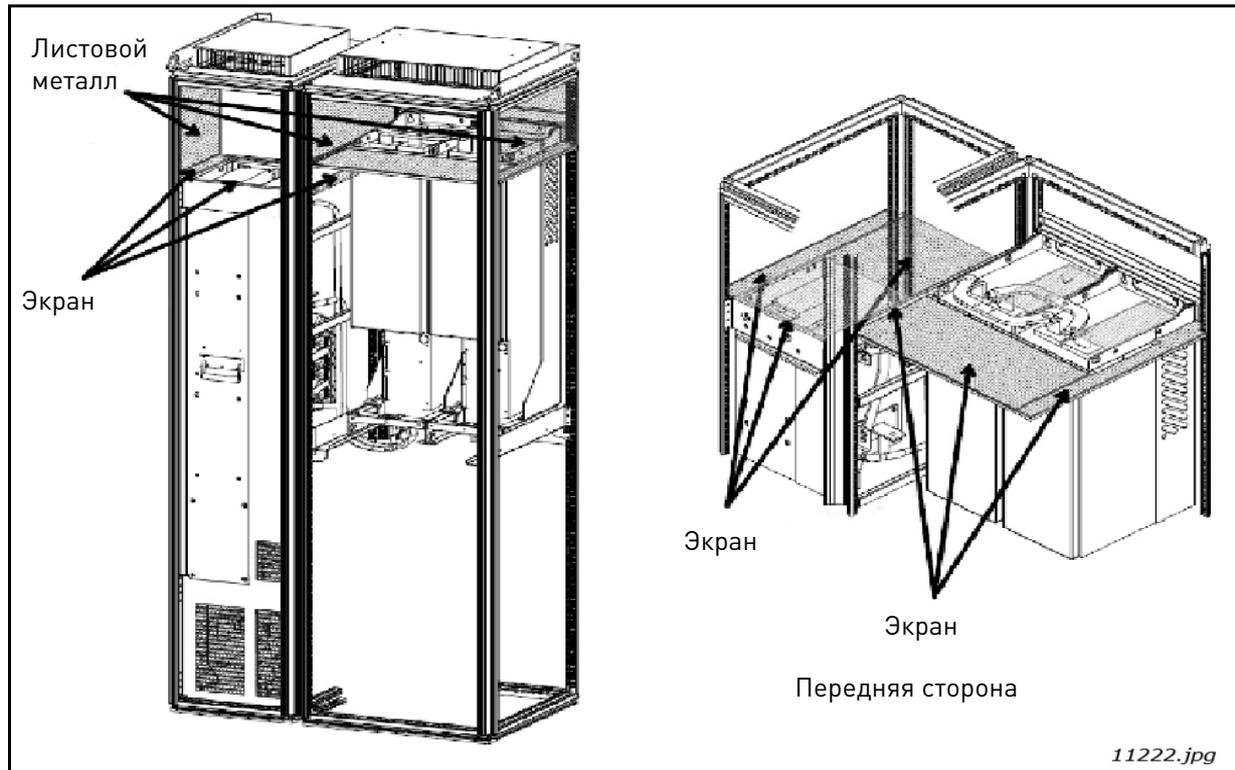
Направляющие охлаждающего воздуха в шкафах для устройства AFE и фильтра LCL типоразмеров FI9 и FI10
